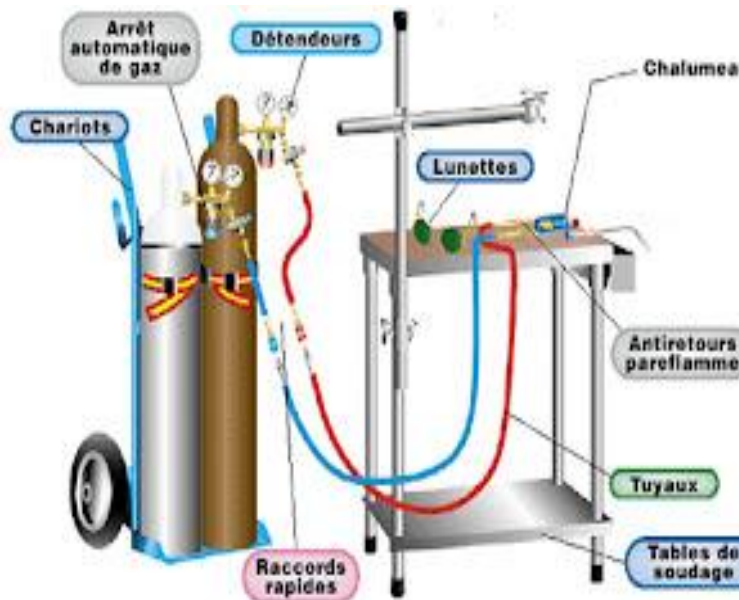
Composition d'une installation de soudage a la flamme
